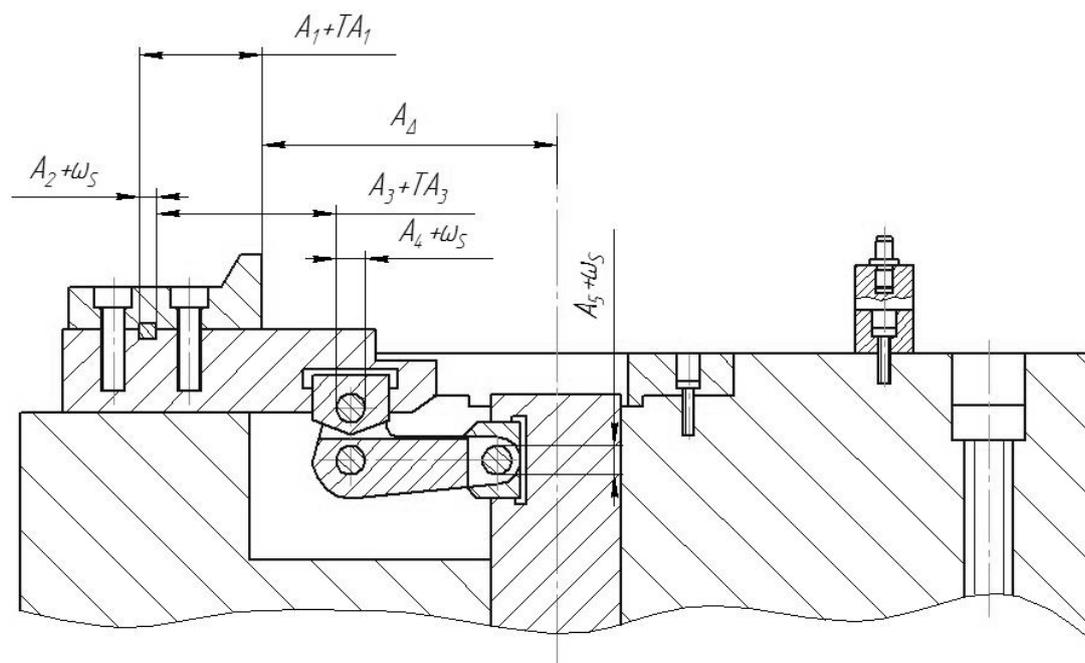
Размерная схема приспособления с рычажным зажимным механизмом
